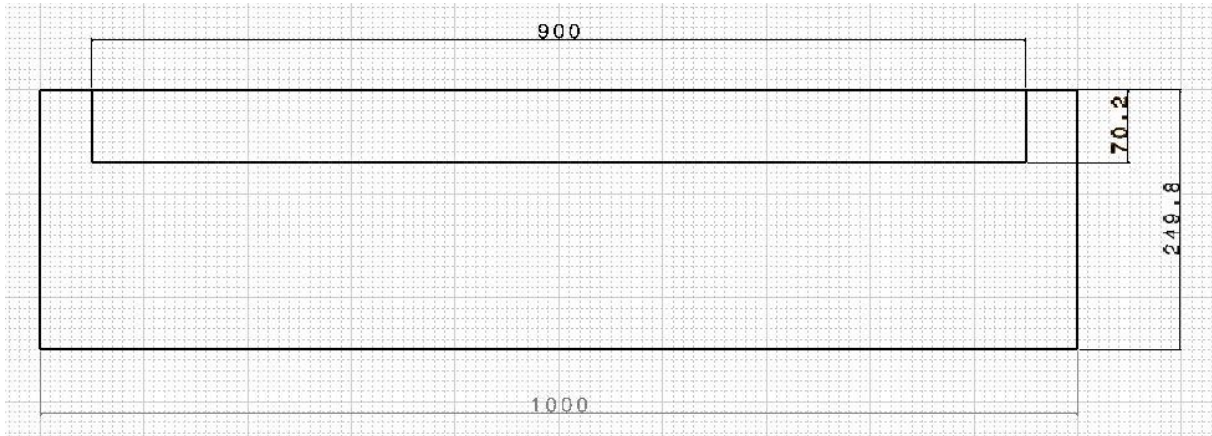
Ön iniş takımı gövde bağlantısı gövde içi
